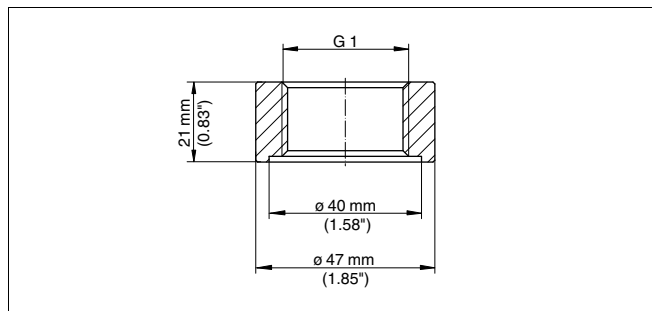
Medidas racor soldado G1 A según DIN 3852-X
